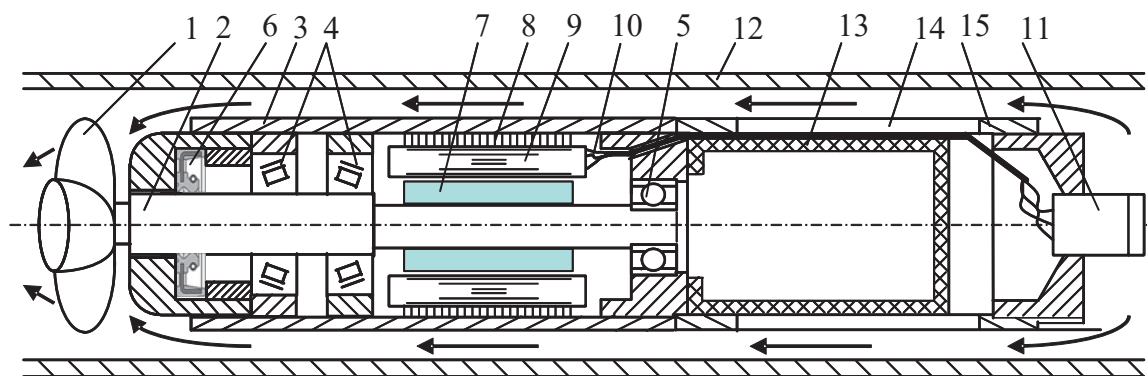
Синхронный генератор забойной инклинометрической телесистемы: 1 – гидротурбина; 2 – вал; 3 – корпус генератора; 4 – радиально-упорные роликовые подшипники; 5 – шариковый подшипник; 6 – сальник; 7 – ротор; 8 – пакет статора; 9 – обмотки статора; 10 – выводы обмоток статора; 11 – герметичный разъем; 12 – переводник; 13 – компенсатор давления; 14 – прорези; 15 – металлический охранный корпус
